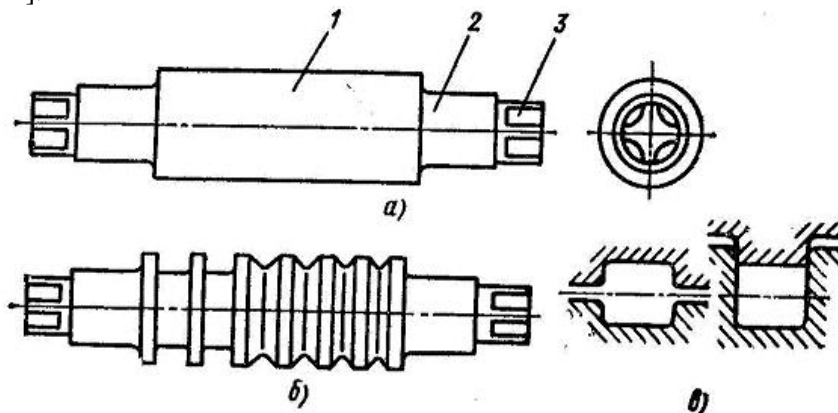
Прокатные валки: а) гладкий валок для листа; б) ручьевого валок для сортового проката: 1 – бочка, 2 – шейки, 3 – трёфы; в) калибры ручьевого прокатного валка: открытый и закрытый
